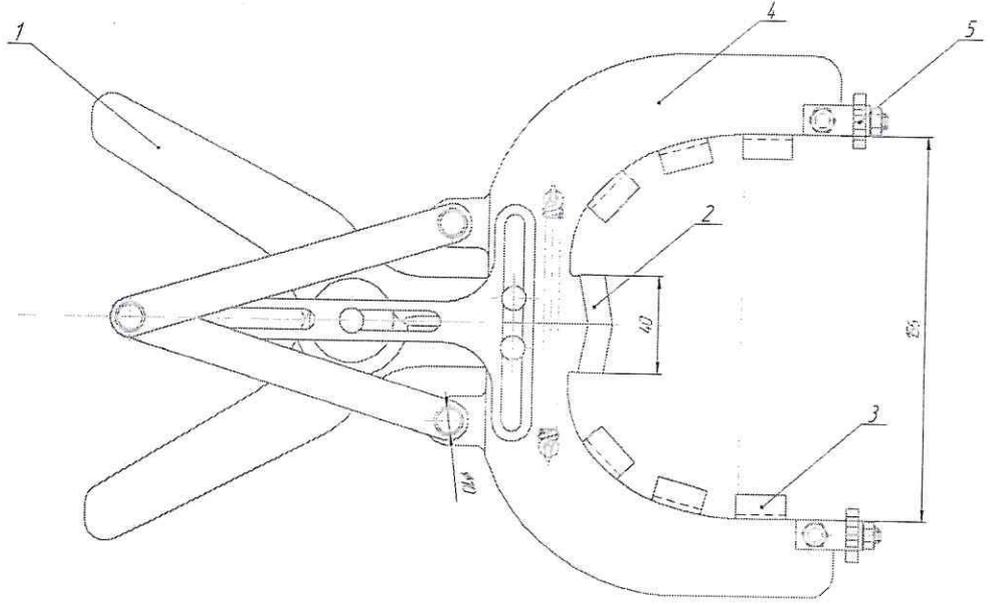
Схема приспособление для замены поршневых колец
